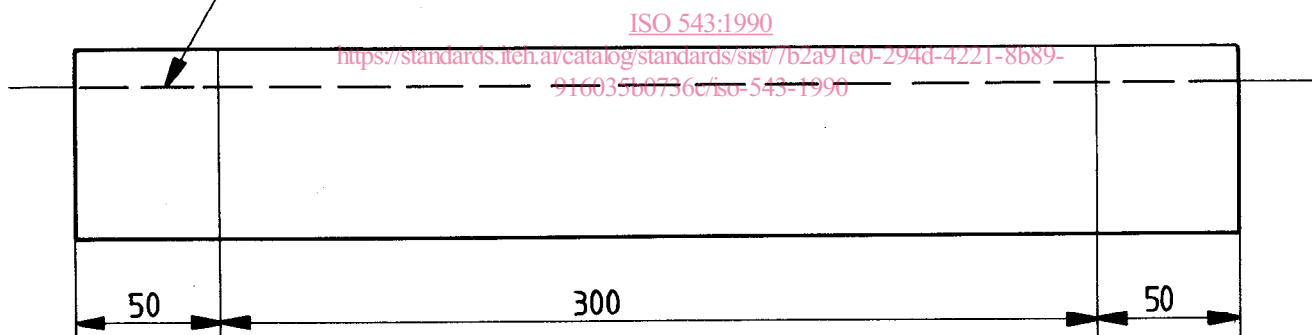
Éprouvette destinée à l'essai de durée de combustion
